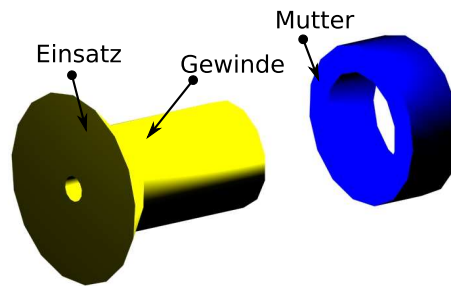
Einsatz mit integrierter Druckbohrung und Gewinde
